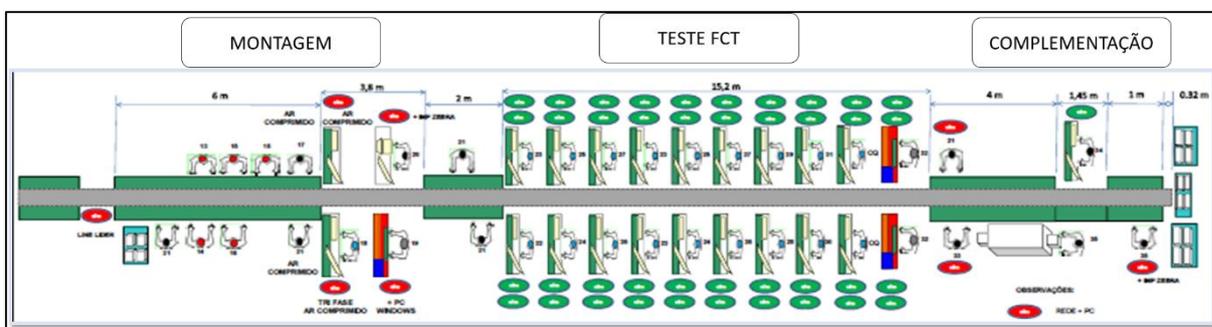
Layout atual da linha referente processo de montagem da placa principal.
